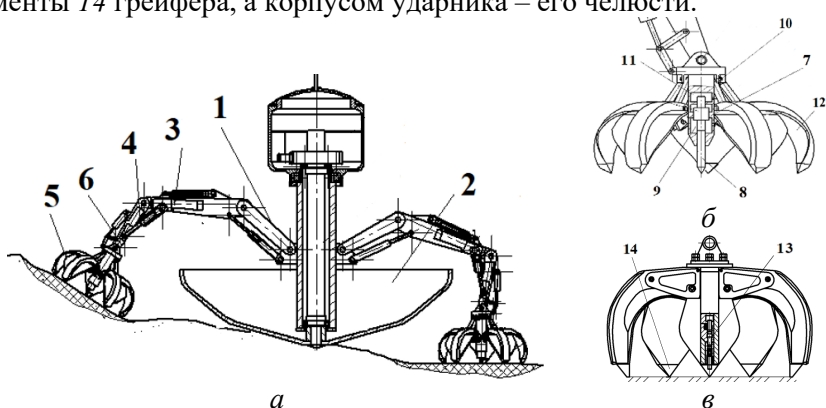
а – конструкция подводного грейферного сборщика; б – конструкция грейфера с встроенным ударником по оси ковша; в – конструкция грейфера с встроенными ударниками в челюстях ковша.
